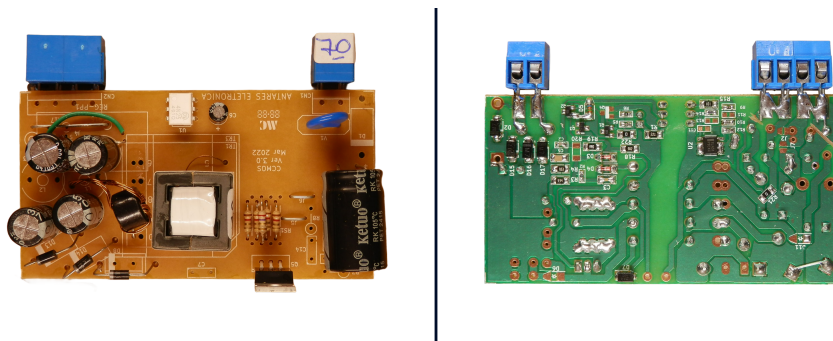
Exemplo de placas eletrônicas utilizadas nos testes, mostrando a face dos componentes (esquerda) e a face da solda (direita) e com os diferentes tipos de componentes e soldas que o sistema deve inspecionar.
